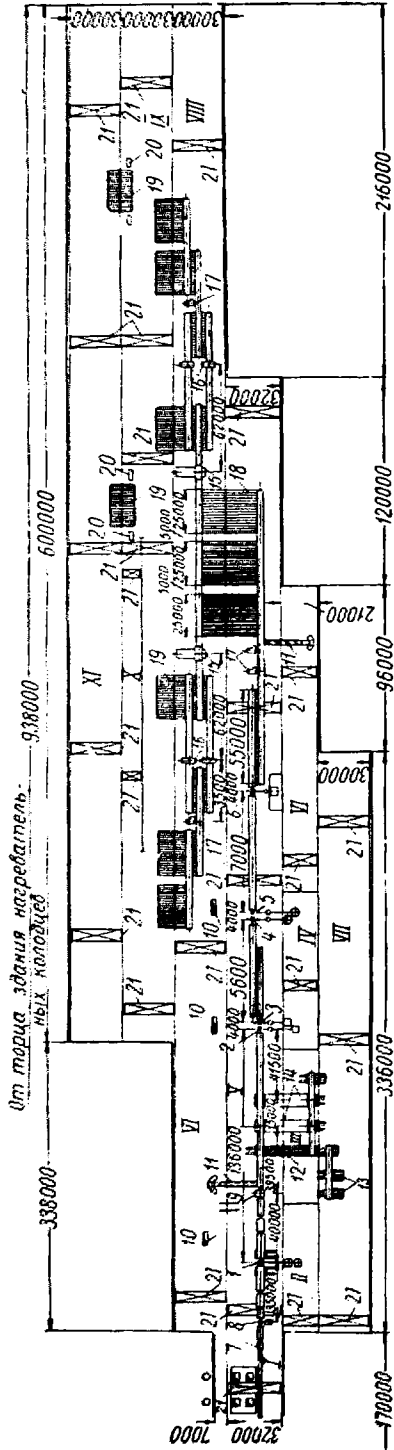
Схема расположения оборудования универсального балочного стана для прокатки широкополочных балок: I — пролет нагревательных колодцев; II — первый машинный зал; III — печной пролет; IV — второй машинный зал; V — пролет стана; VI — скрапный пролет; VII — склад блюмов и слэбов; VIII — пролет отделки; IX — пролет уборки; X — пролет ремонта; XI — склад готовой продукции; 1 — обжимная клетка блюминга 1475; 2 — черновая клетка дуо; 3 — черновая универсальная клетка; 4 — промежуточная универсальная клетка; 5 — промежуточная клетка дуо; 6 — чистовая универсальная клетка; 7 — тележка-опрокидыватель; 8 — поворотный стол; 9 — ножницы; 10 — ямы для уборки окатышей; 11 — транспортер обрезков; 12 — передаточные шпелтеры; 13 — стеллажи; 14 — методические печи; 15 — правильные машины; 16 — правильные прессы; 17 — салазковые пилы; 18 — холодильники; 19 — стеллажи; 20 — фрезерные станки; 21 — кран
